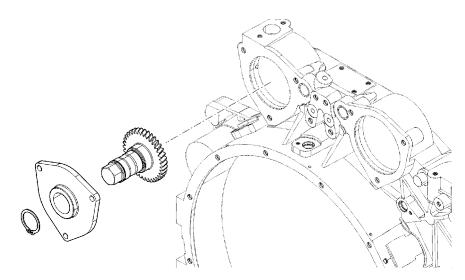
Dispositivo de giro - Montaje de la toma de fuerza NA2, herramienta especial núm. 30e
